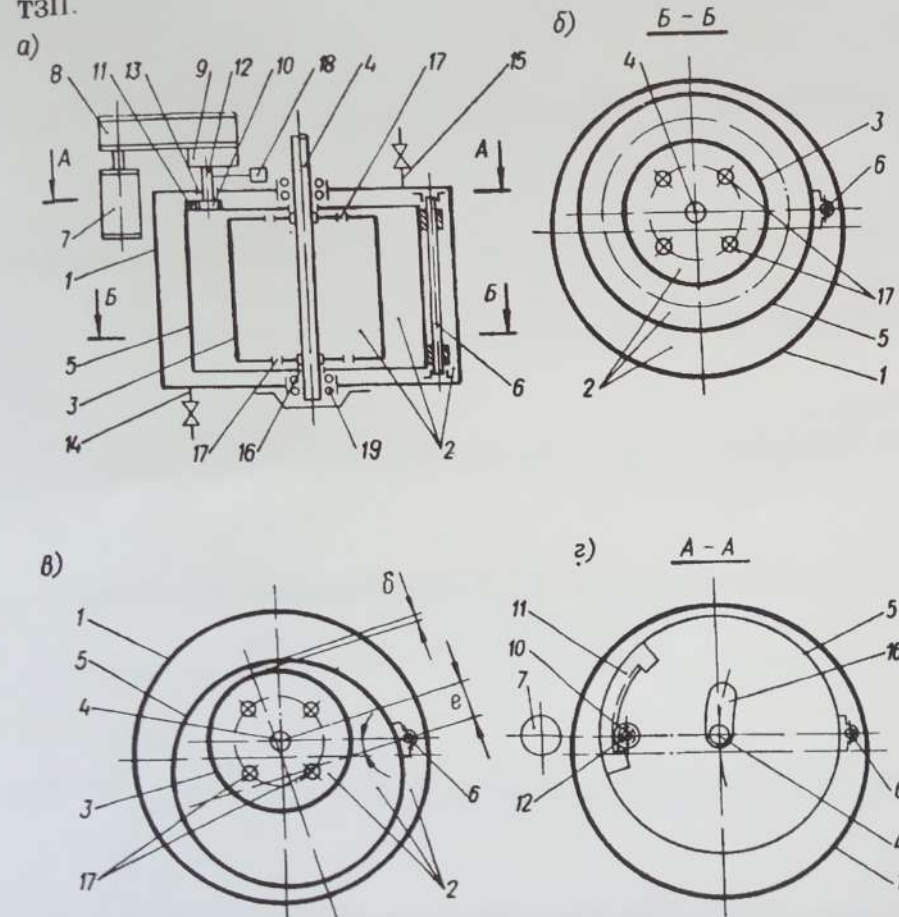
Схема гідрогальма [10]: а - осьовий розріз; б - поперечний розріз при співвісному положенні ротора і статора; в - те ж, при неспіввісному положенні; г - поперечний розріз з елементами механізму для переміщення статора: 1 - корпус; 2 - робоча рідина; 3 - ротор; 4 - вал ротора; 5 - статор; 6 - вісь статора; 7 - привід статора; 8 - редуктор; 9 - реверс; 10 - шестерня; 11 - зубчастий сегмент; 12 - вал реверса; 13 - сальник; 14 і 15 - патрубки; 16 і 17 - отвори; 18 - лічильник числа обертів вала 12; 19 - підшипник.
